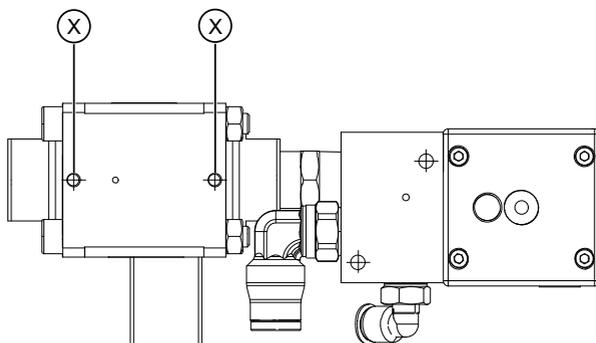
1-Gas-Ausführung, Befestigung Schaltventil (optional), Gewinde M4
